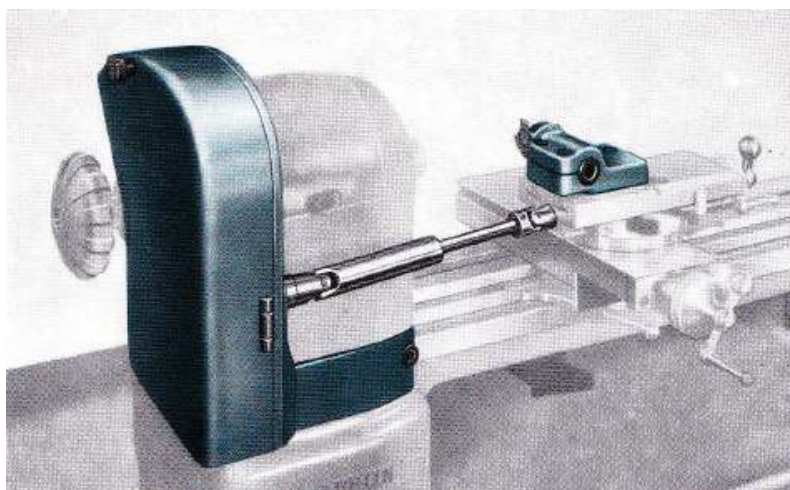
Screw-cutting by carriage and universal shafts*, [9].
